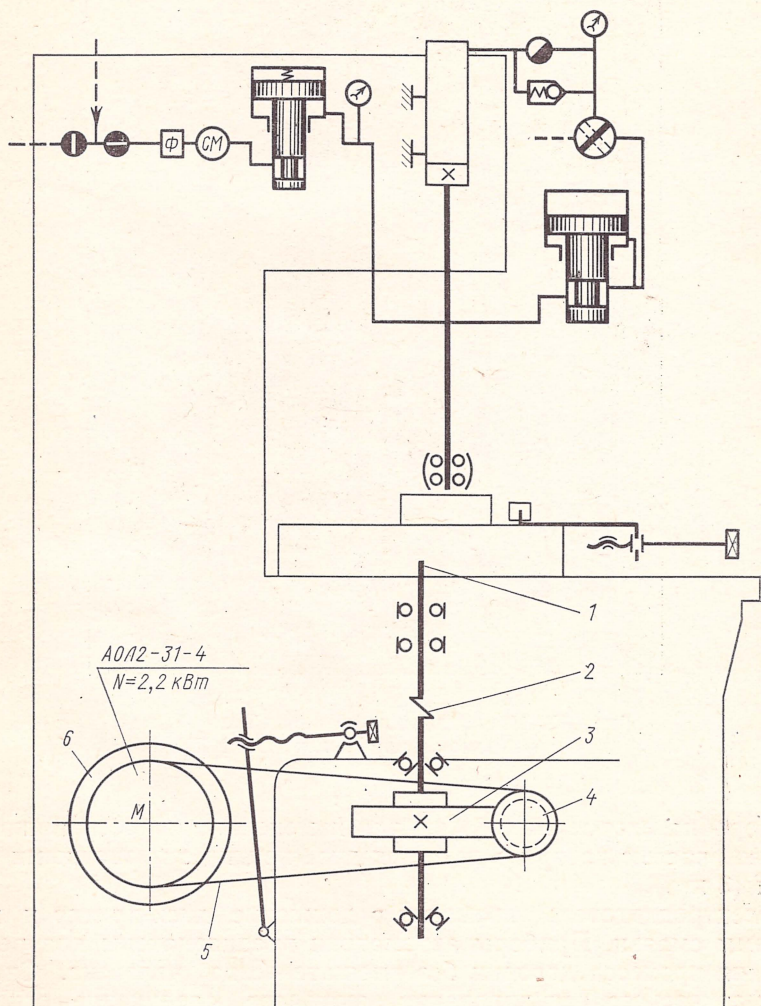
Кинематическая схема плоскодвигательного станка 3806Л.
